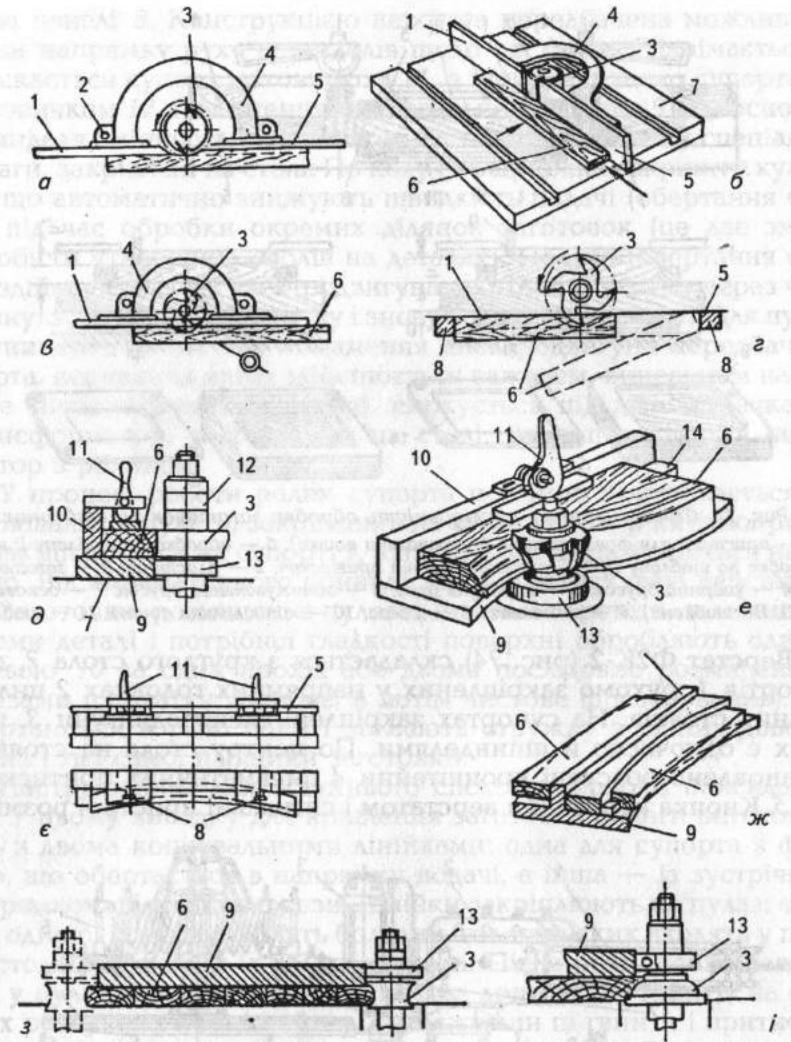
Схема обробки деталей на копіювально-фрезерних верстатах:
